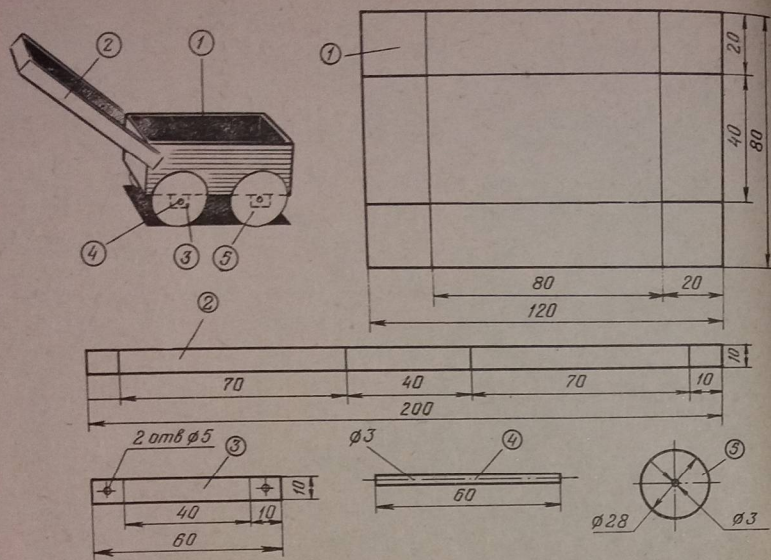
Модель тележки: 1—корпус; 2—ручка; 3—подшипник; 4—ось; 5—колесо
